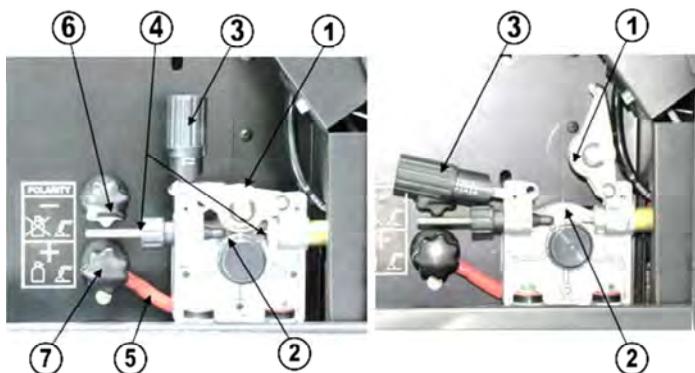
Механизм подачи сварочной проволоки:
